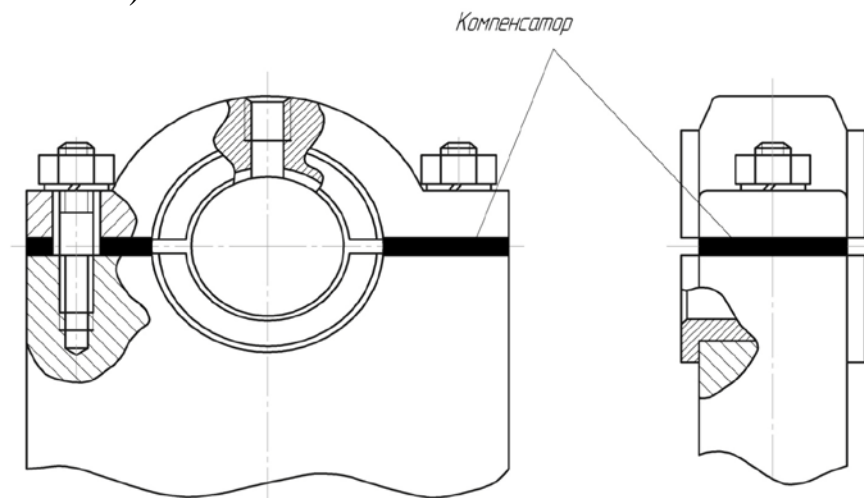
Способ регулировки радиального зазора в подшипнике скольжения
